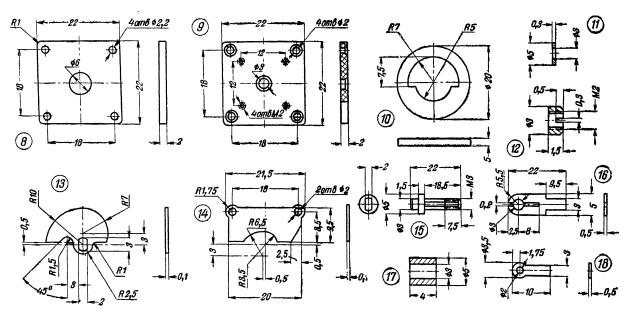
Конструкция и детали блока переменных конденсаторов.
